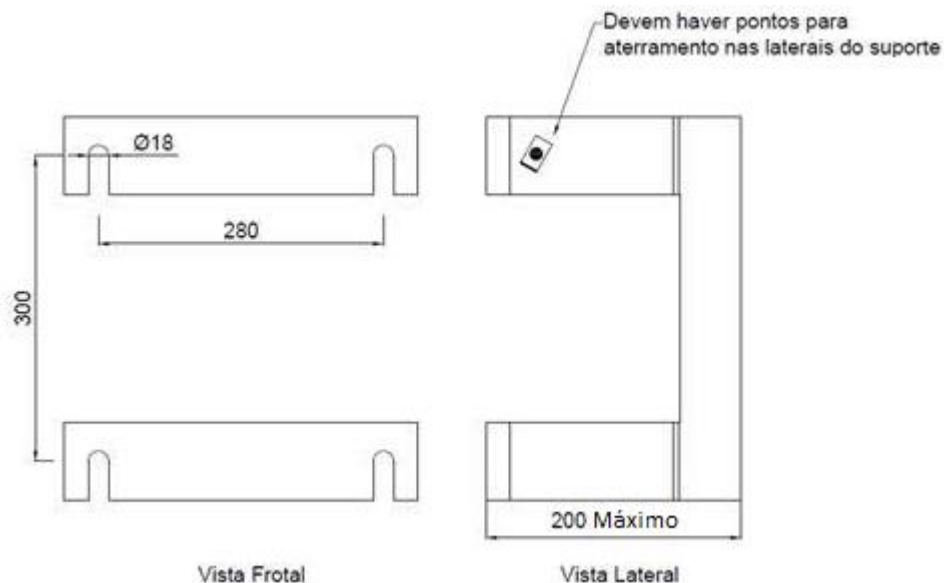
Dimensões do suporte de fixação do Conjunto de Medição.
